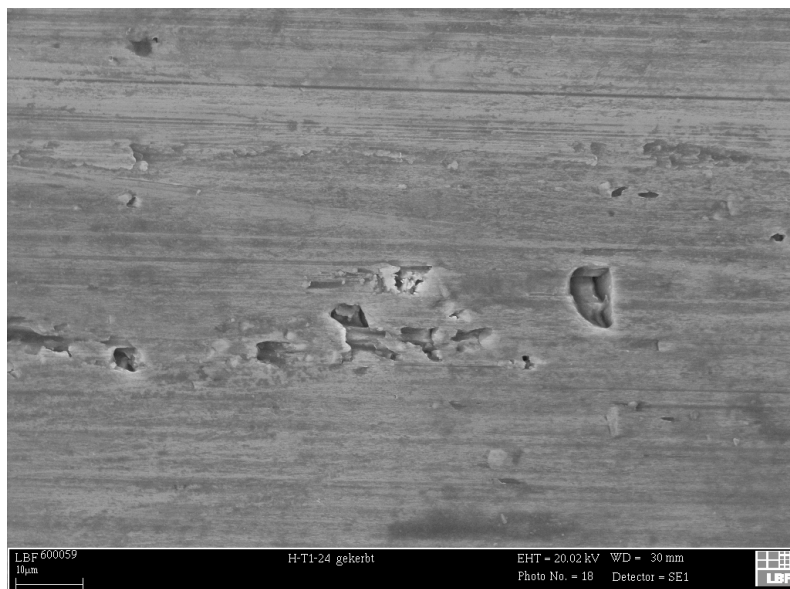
„Stand der Technik“, Ausbrüche auf der Oberfläche;
